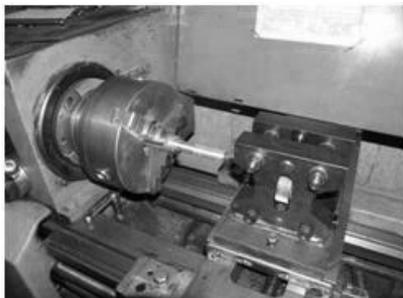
Станочное приспособление для накатывания мелкозубчатых колес
